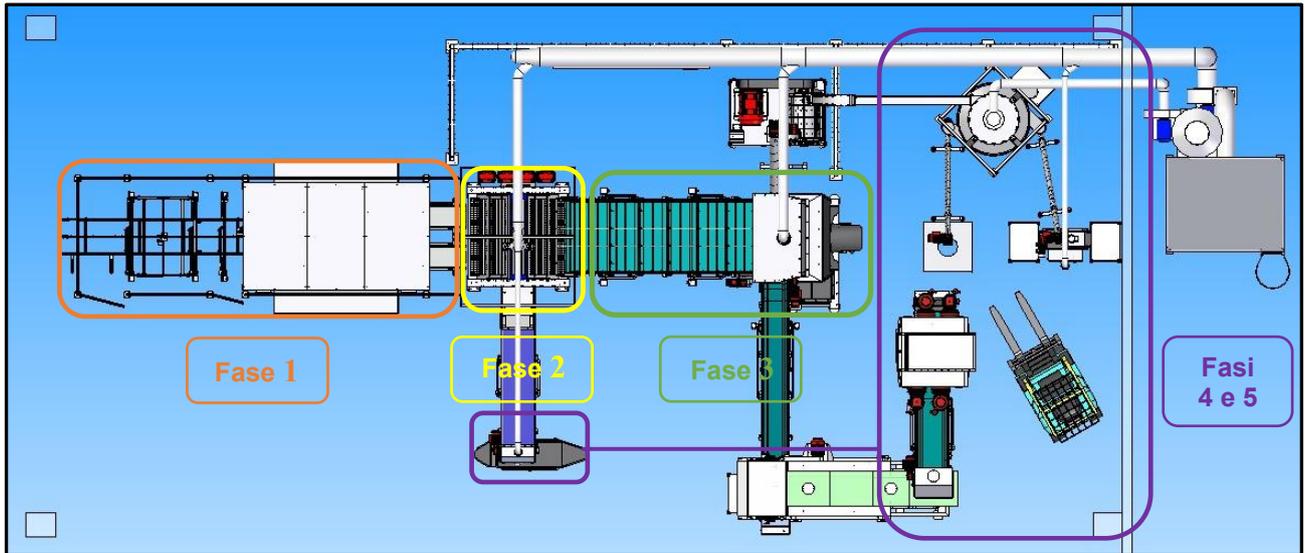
Layout dell'impianto di trattamento RAEE con individuazione delle fasi di processo
